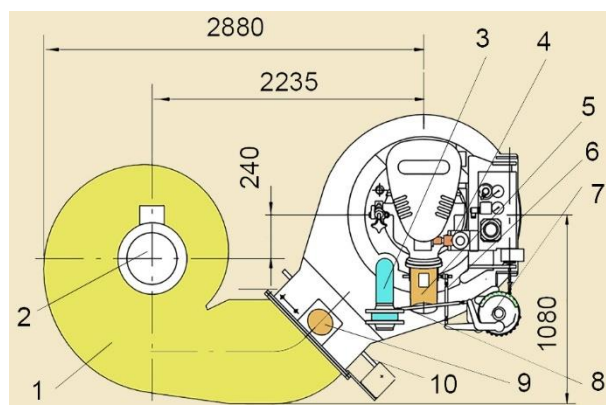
Расположение форсуночного агрегата на фронте котла
